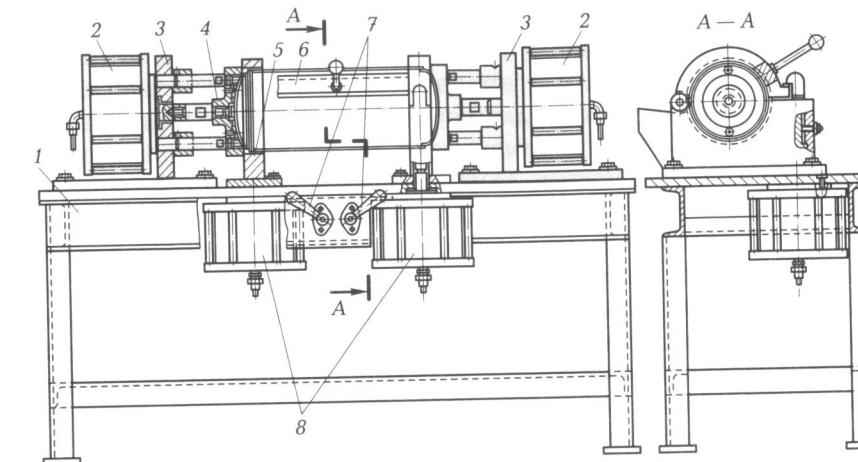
Приспособление для сборки обечеек с днищами:
